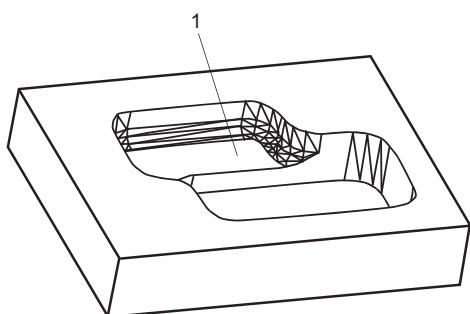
Конструктивный элемент 1 заготовки, получаемый фрезерованием
